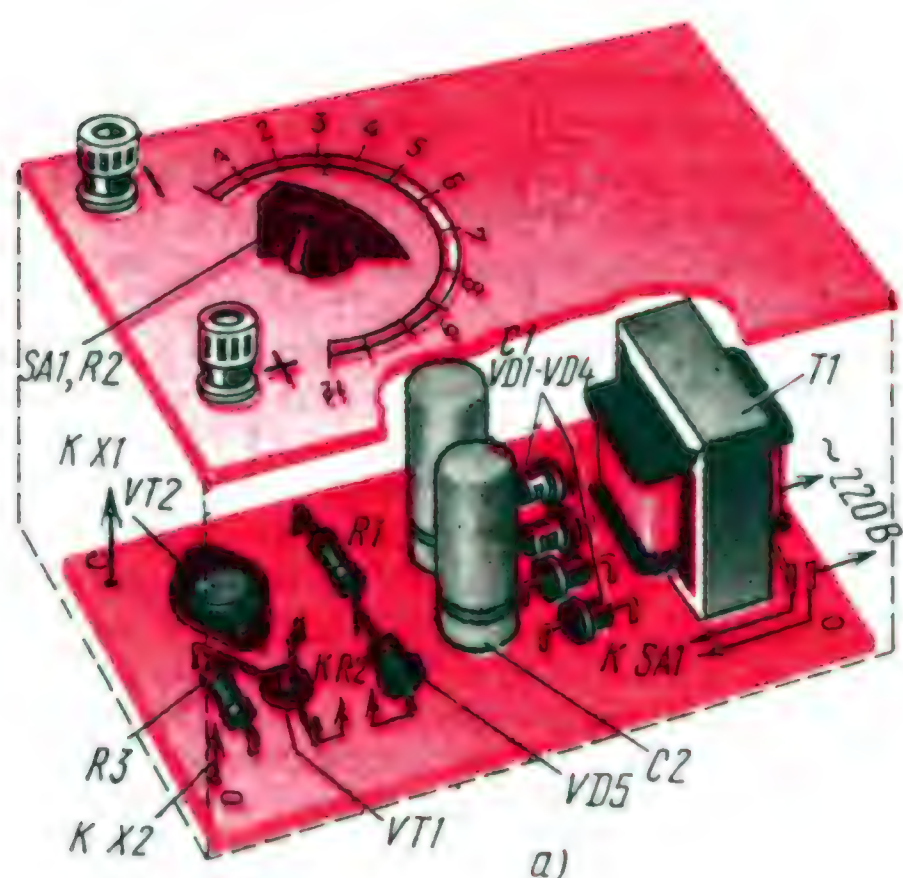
Конструкция сетевого блока питания и схема соединения деталей на монтажной плате
